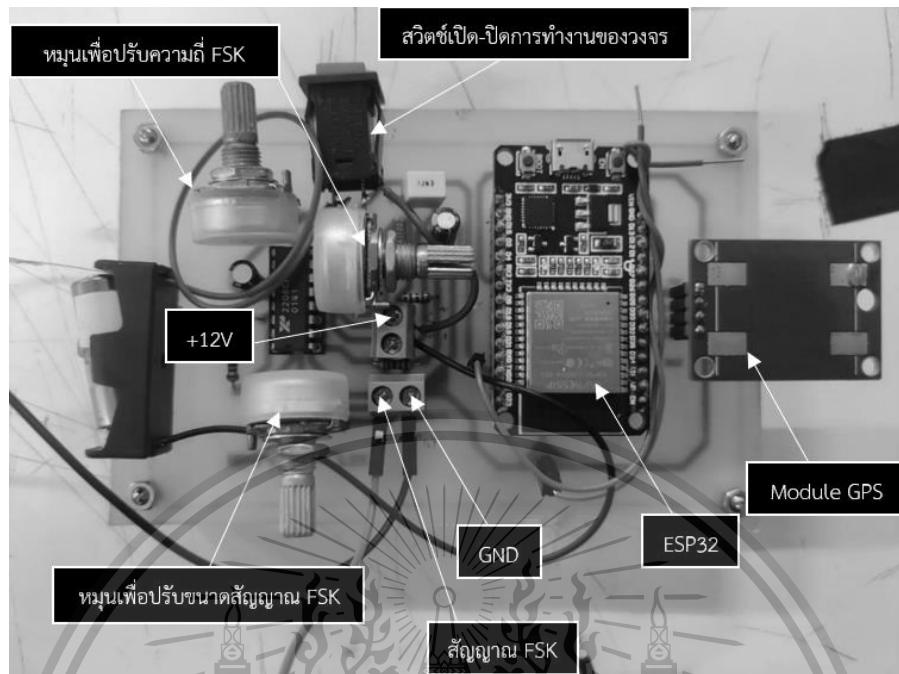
PCB ของวงจร FSK Modulator
